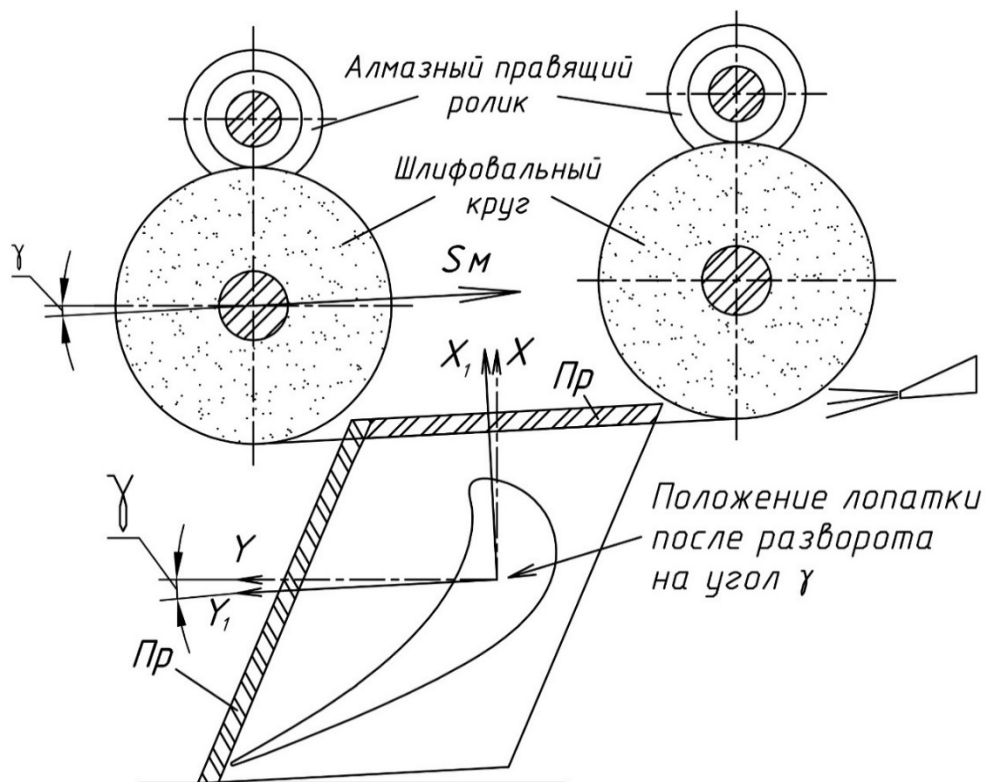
Для обработки установочных поверхностей лопатки, развёрнутое на угол положение лопатки
